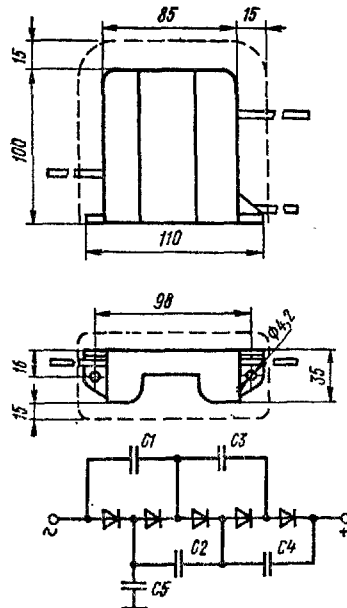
Общий вид, габаритные, присоединительные размеры и электрическая схема умножителя УН7,5/20-0,2
